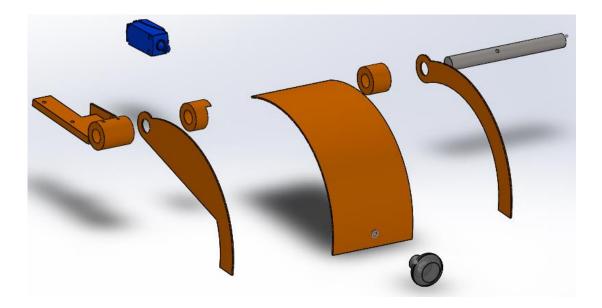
Vista explosionada del resguardo del cabezal y plato.
